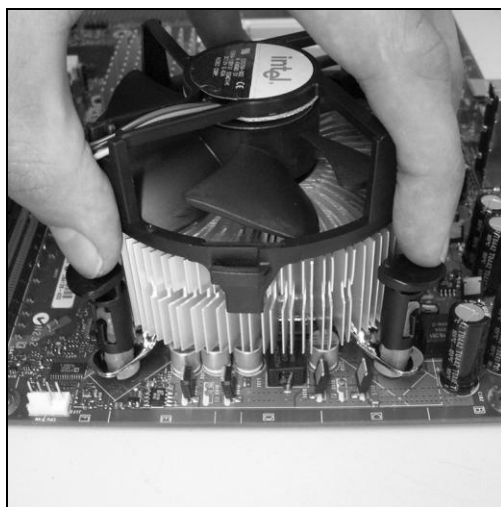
Проверка правильности установки кулера для процессора в корпусе LGA
